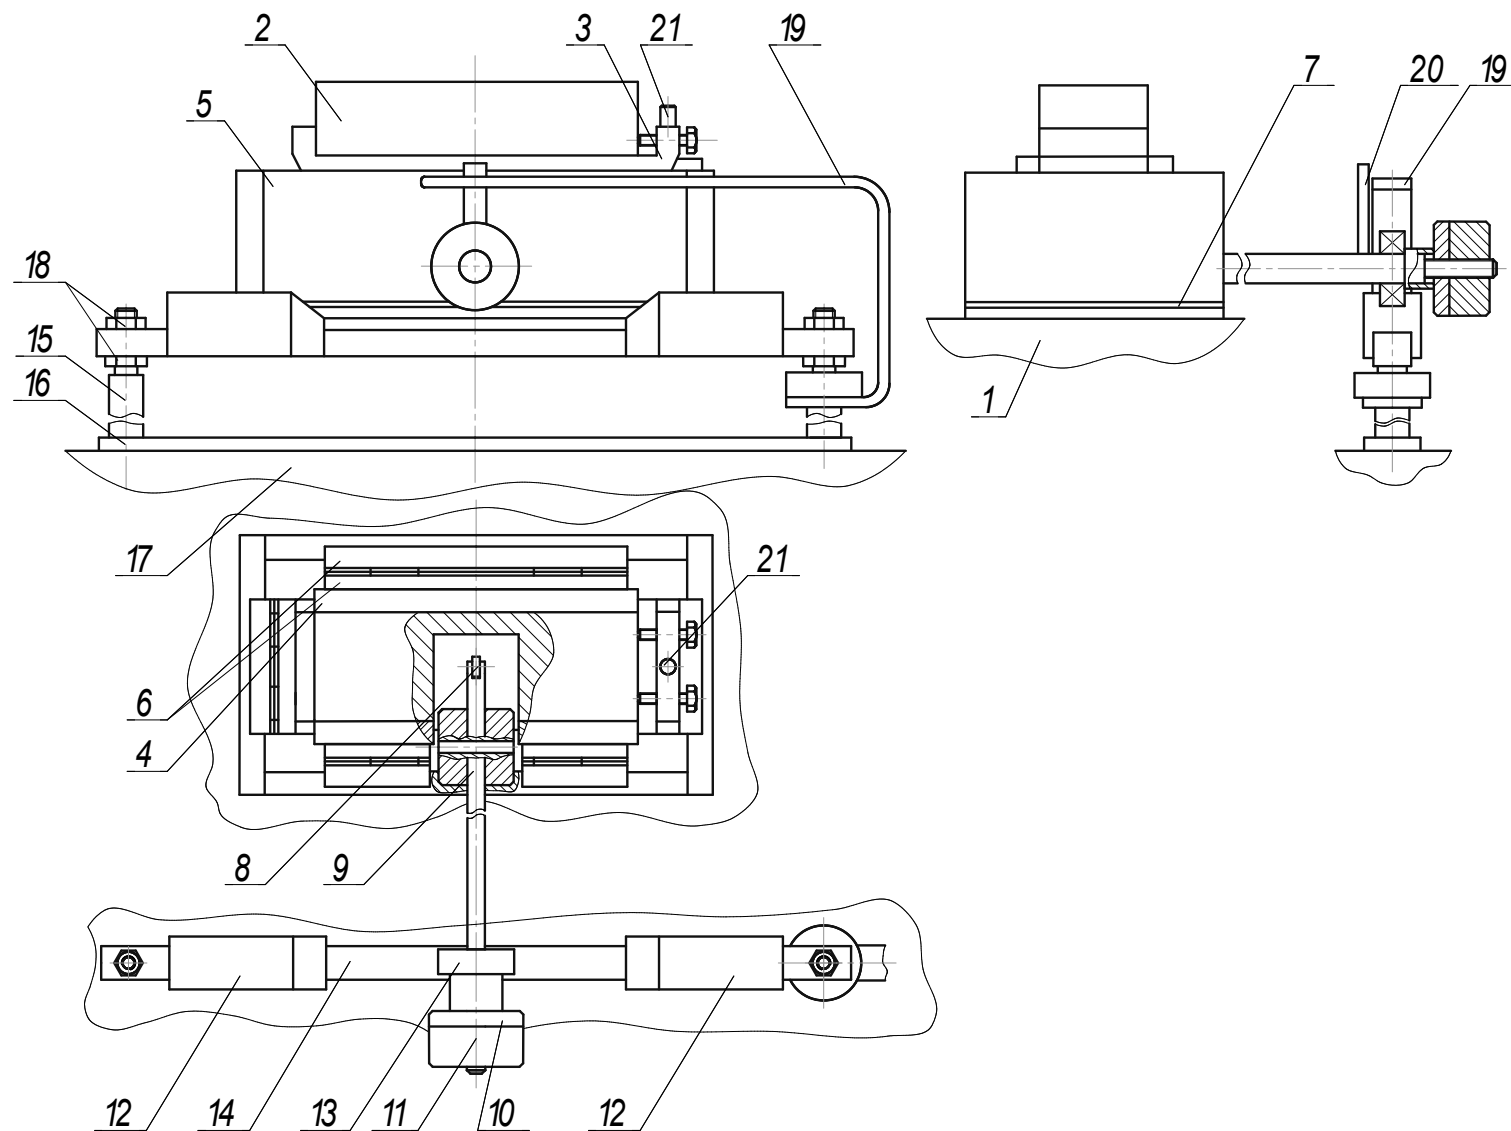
Конструкция приспособления для плоского шлифования с постоянной силой поджима заготовки P_n
